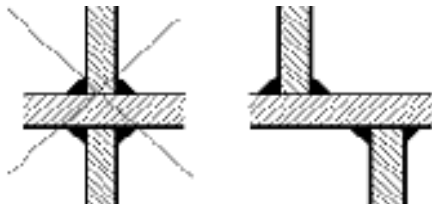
Приварка ребер. Ребра розміщені в шаховому порядку
